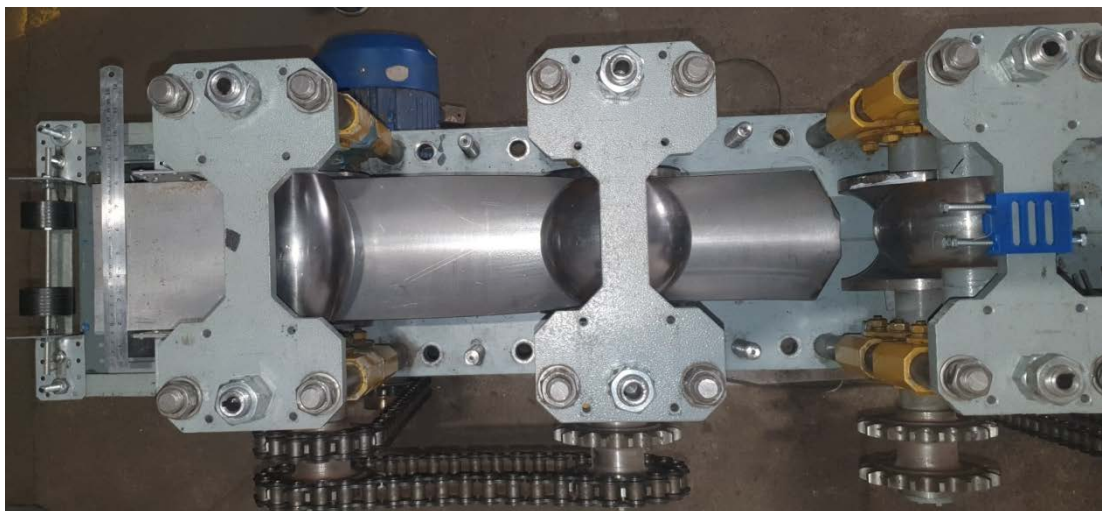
Сформованная трубная заготовка в приводных клетях стана
